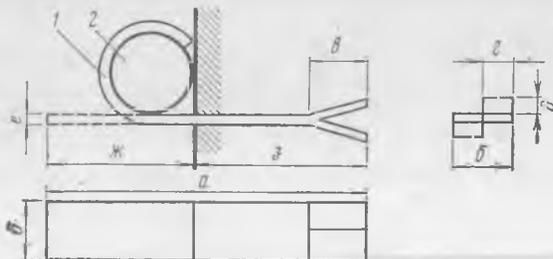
Внешний вид пластинчатых скреп: 1 — скрепа; 2 — кабель
